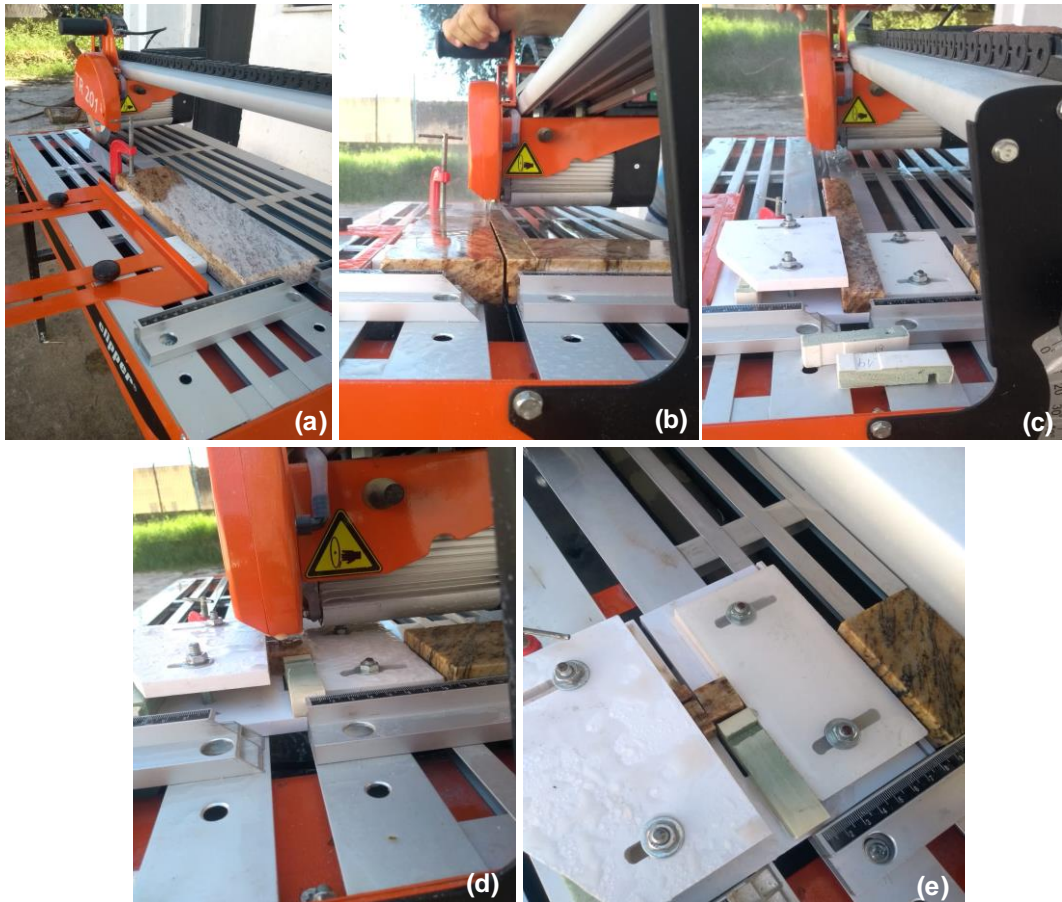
Sequência de corte do material rochoso na máquina utilizada. (a) Posicionamento do gabarito para corte das chapas menores; (b) corte do filete; (c) ajuste das dimensões do filete; (d) corte dos cubos; (e) cubo pronto.
